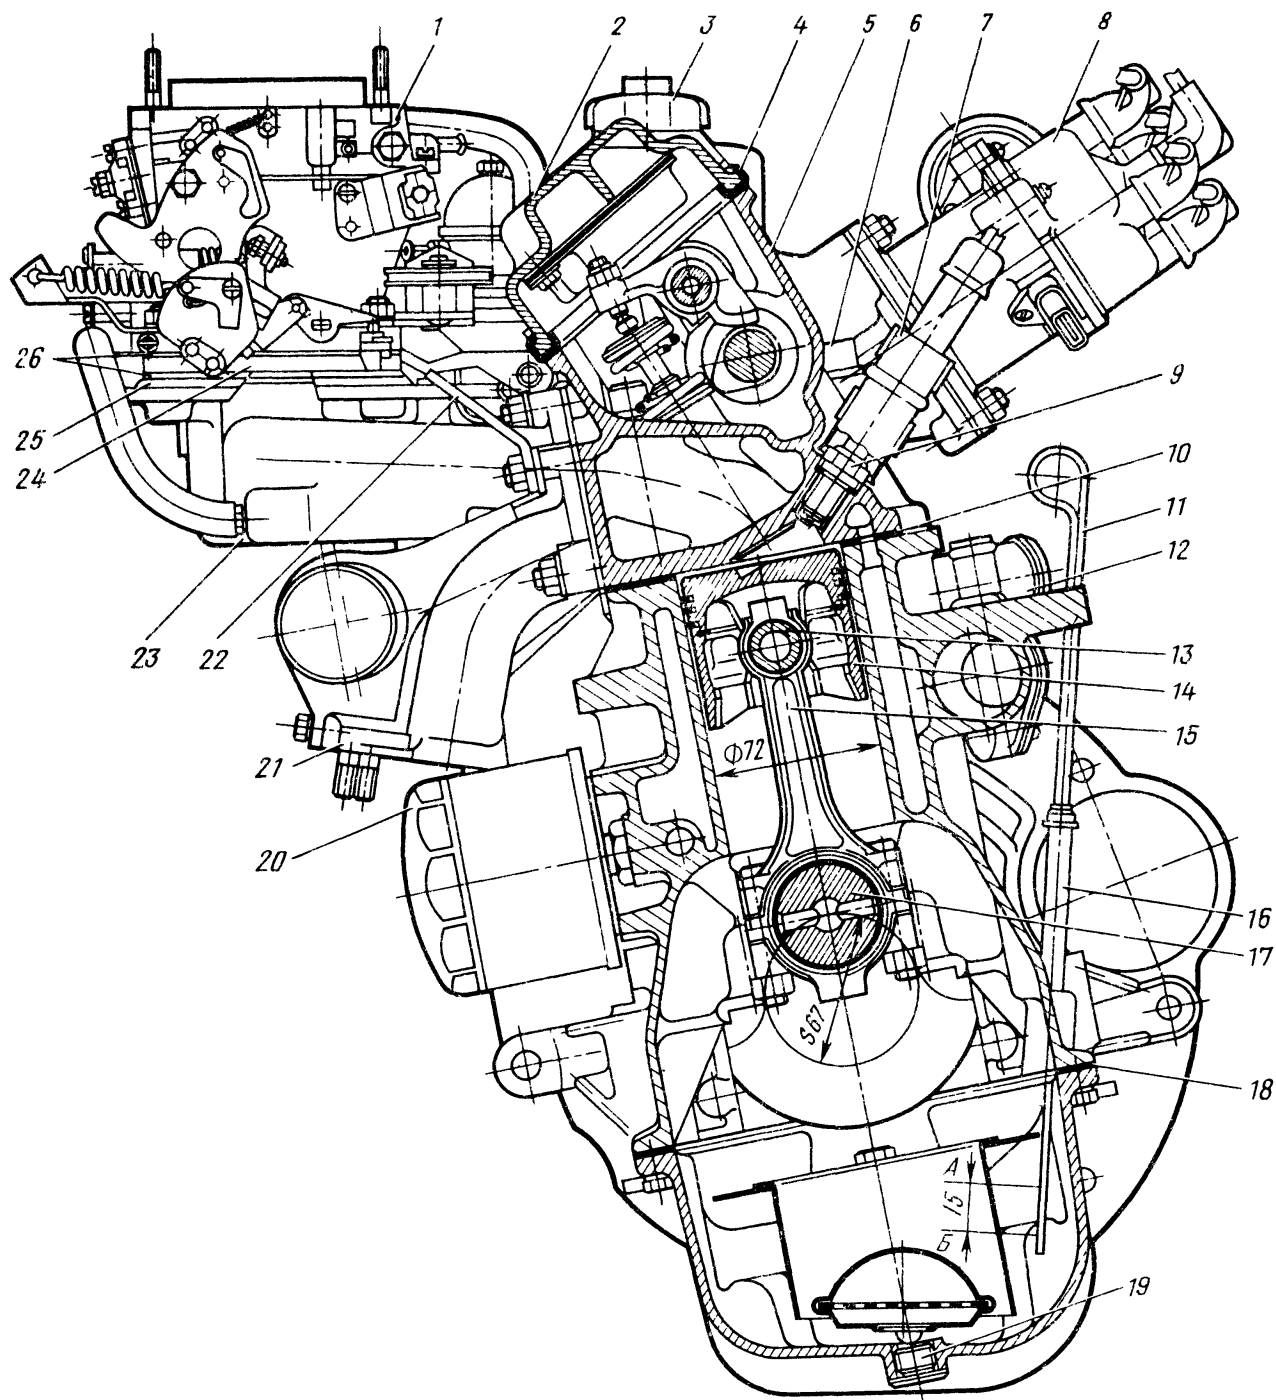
Поперечный разрез двигателя МеМ3-245:
